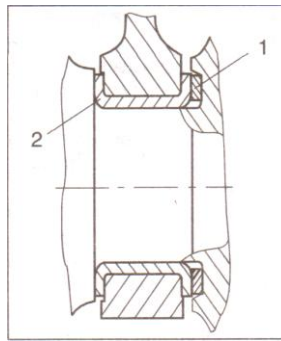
Конструкция ремонт упорного подшипника коленчатого вала: 1 — дополнительные полукольца, установленные в расточку на поврежденном торце коленчатого вала; 2 — штатный вкладыш с упорными полукольцами
